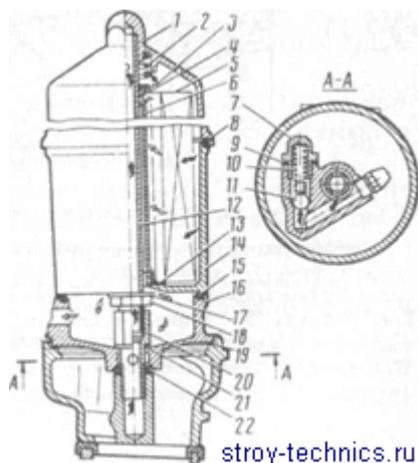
Масляный фильтр двигателей 3МЗ-5 3, -66:
